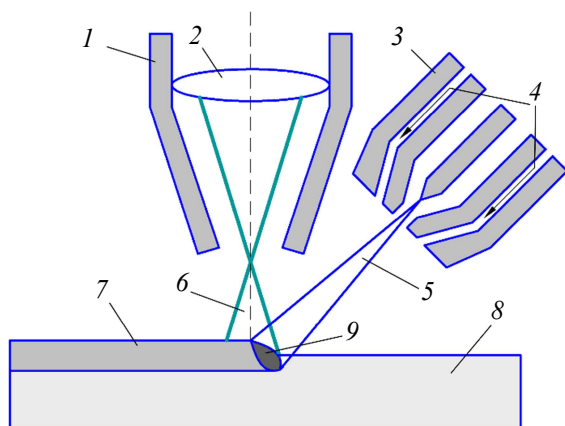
Схема процесса порошковой лазерно-плазменной наплавки с использованием плазмотрона прямого действия: 1 – лазер; 2 – фокусирующая линза; 3 – плазмотрон прямого действия; 4 – подача газа с наплавочным порошком; 5 – плазменный факел; 6 – лазерный пучок; 7 – наплавленное покрытие; 8 – металлическая подложка; 9 – область воздействия плазменного факела и лазерного пучка
